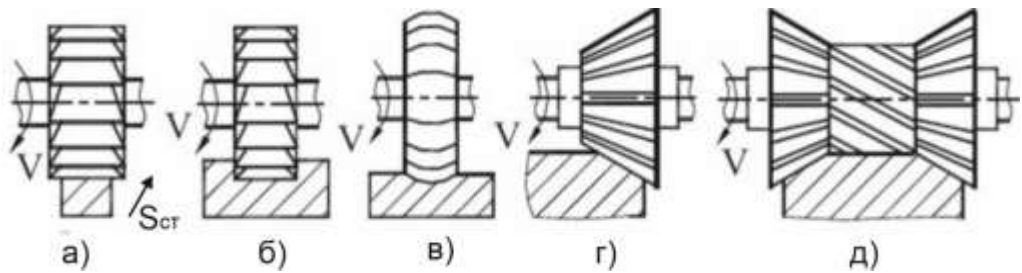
Схеми фрезерування дисковими фрезами.
